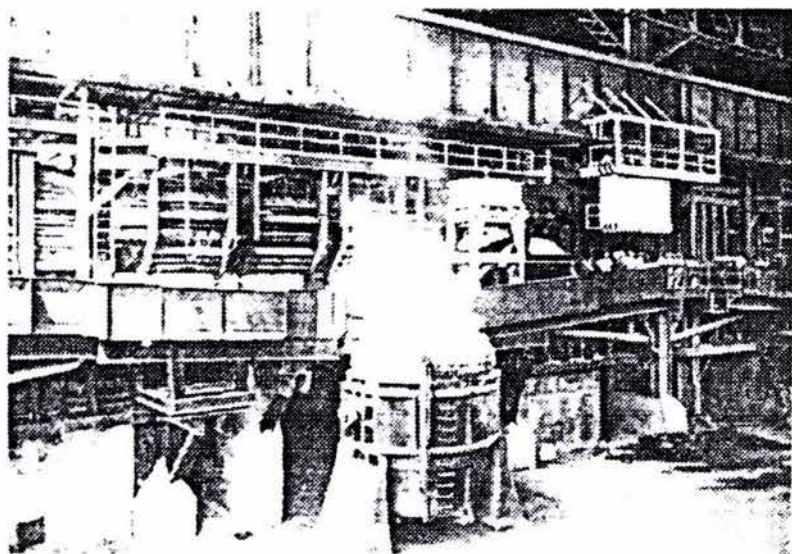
Vaciado de 275 Ton de acero para rieles en el departamento No.2 de Aceración, instalado recientemente.
